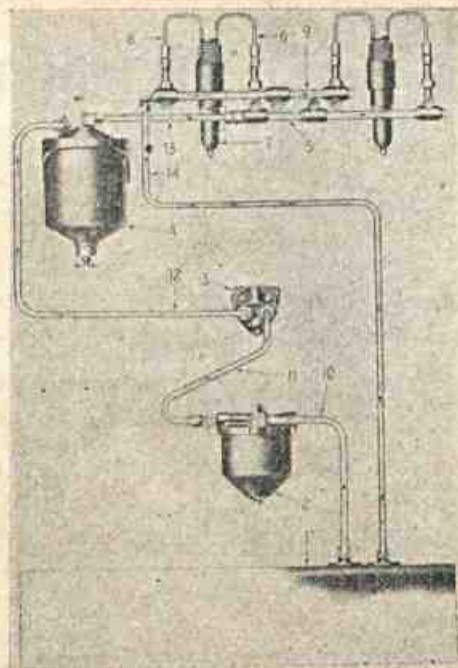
Sistema de combustível do motor Diesel do tipo General Motors. 1 — Tanque de combustível. 2 — Filtro primário. 3 — Bomba de combustível. 4 — Filtro secundário. 5 — Tubo de admissão inferior. 6 — Tubo de admissão ao injetor. 7 — Injetor. 9 — Tubo superior de saída. 10 — 11 — 12 — 13 e 14 — Canos de combustível.
